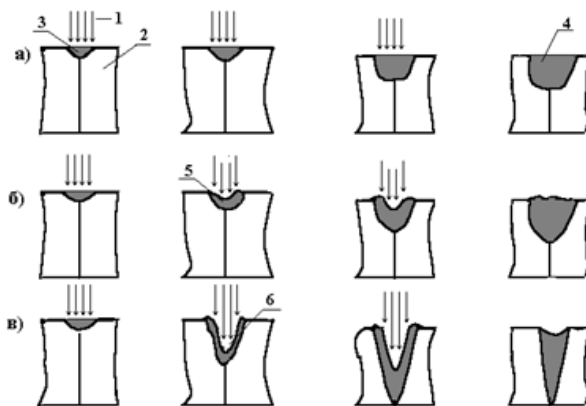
Стадии проплавки соединяемых деталей: 1 – лазерное излучение; 2 – детали; 3 – расплав; 4 – сварочная ванна; 5 – заглубление; 6 – отверстие, образованное вследствие перехода расплава в газообразную фазу; а – 10^5 – 10^6 Вт/см², б – $5 \cdot 10^5$ – $5 \cdot 10^6$ Вт/см², в – 10^6 – 10^7 Вт/см²
